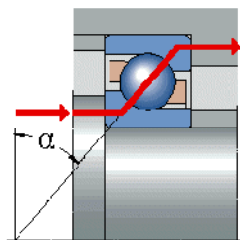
Ángulo de contacto en rodamientos de bolas con contacto angular
